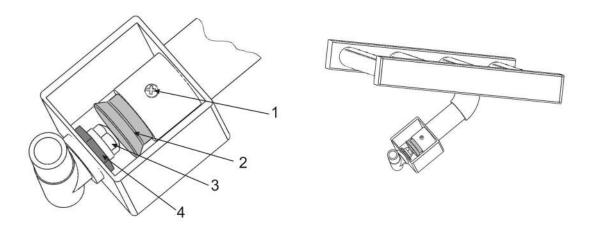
Устройство горелок шашлычницы 1 – винт крепления цилиндра шибера; 2 – цилиндр шибера; 3 – сопло; 4 – прижимная гайка.
